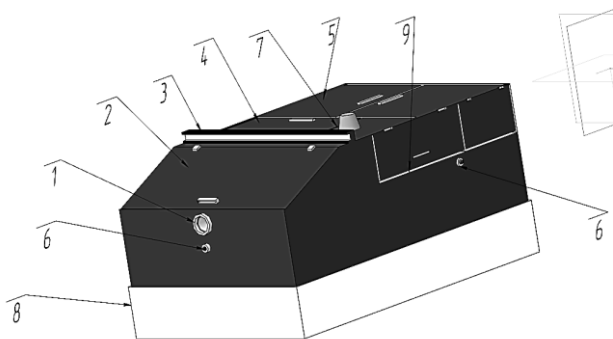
Схема корпуса: 1 – входной патрубок 2 – крышка обслуживания бака – сепаратора 3 – фонарь диодный 4 – крышка обслуживания мотопомпы 5 – крышка обслуживания мотопомпы и аккумуляторов 6 – видекамера 7 – проблесковый маячок 8 – алюминиевые защитные листы 9 – боковые крышки обслуживания ЭБУ и аккумуляторов
